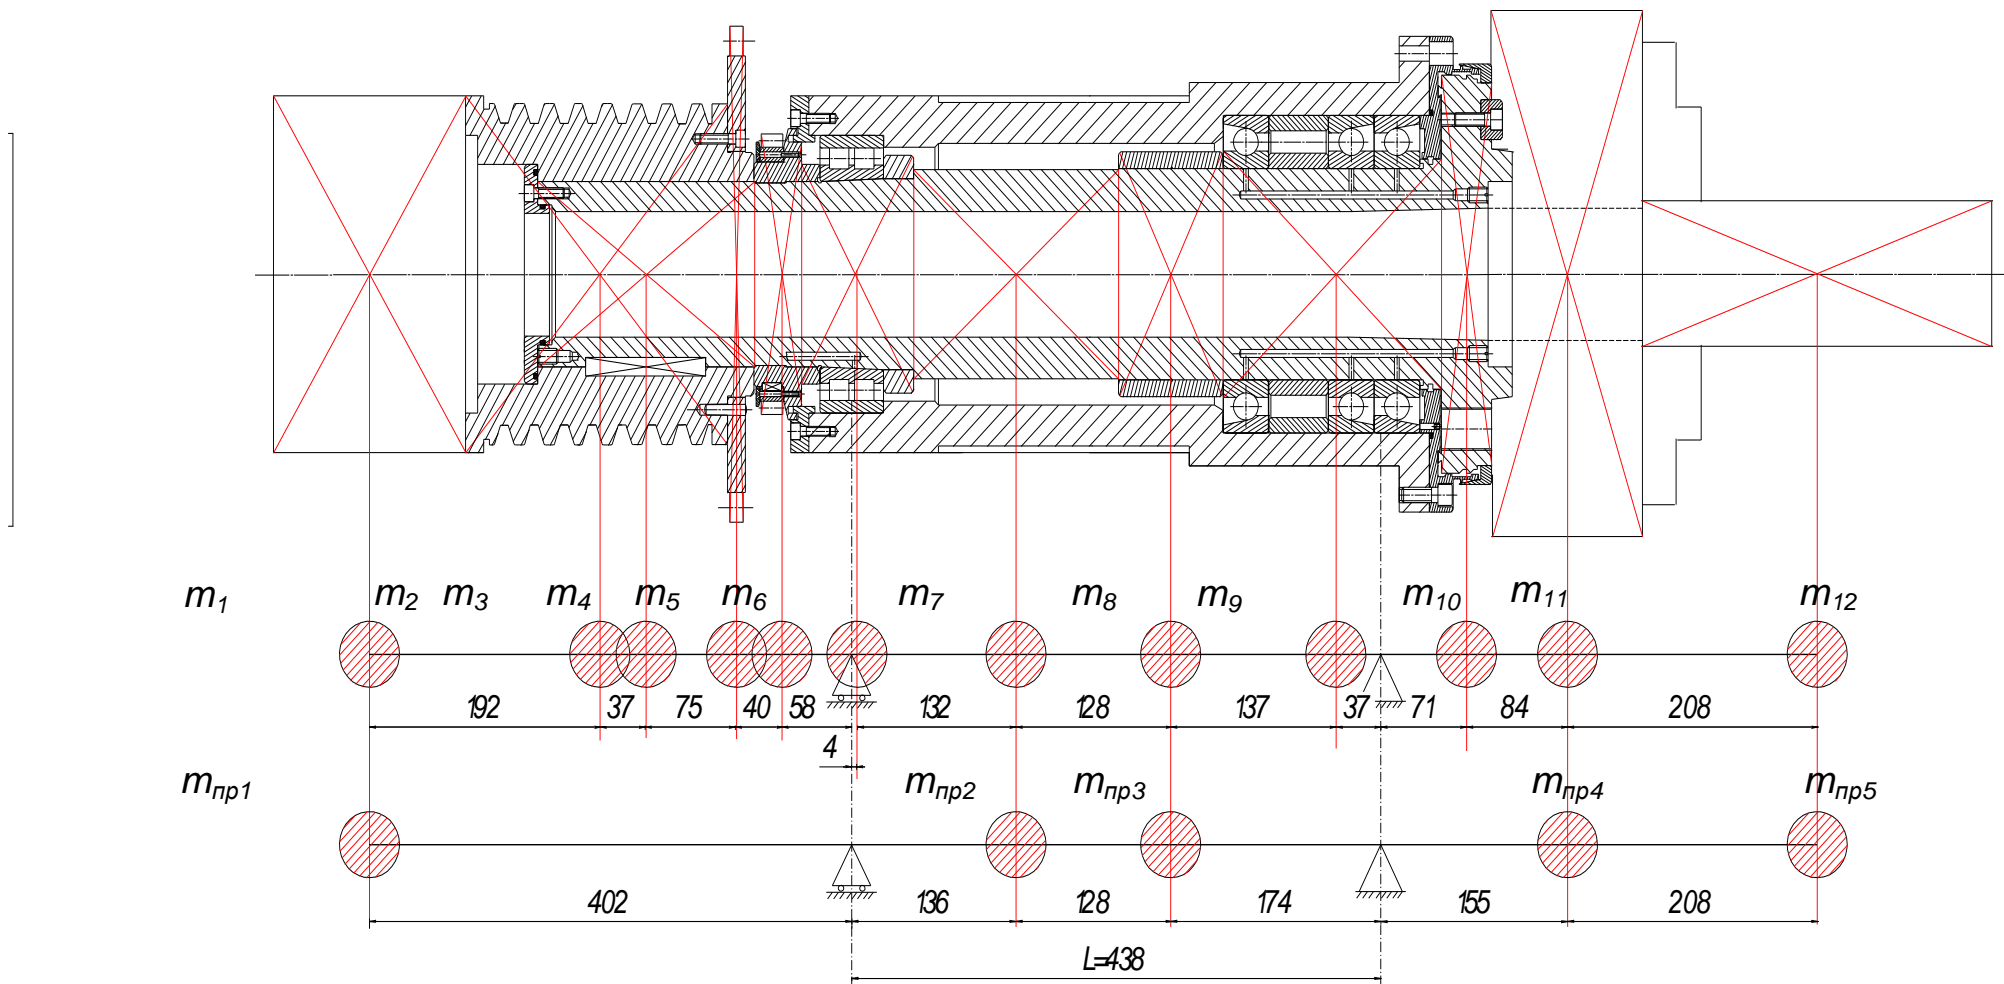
Шпиндельний вузол токарного патронно-центрового верстата з ЧПК мод. SPU 40 CNC при затиску заготовки в патроні: а) конструкція шпиндельного вузла із затискним патроном та гідроциліндром затиску; б) вихідна динамічна модель; в) приведена динамічна модель
